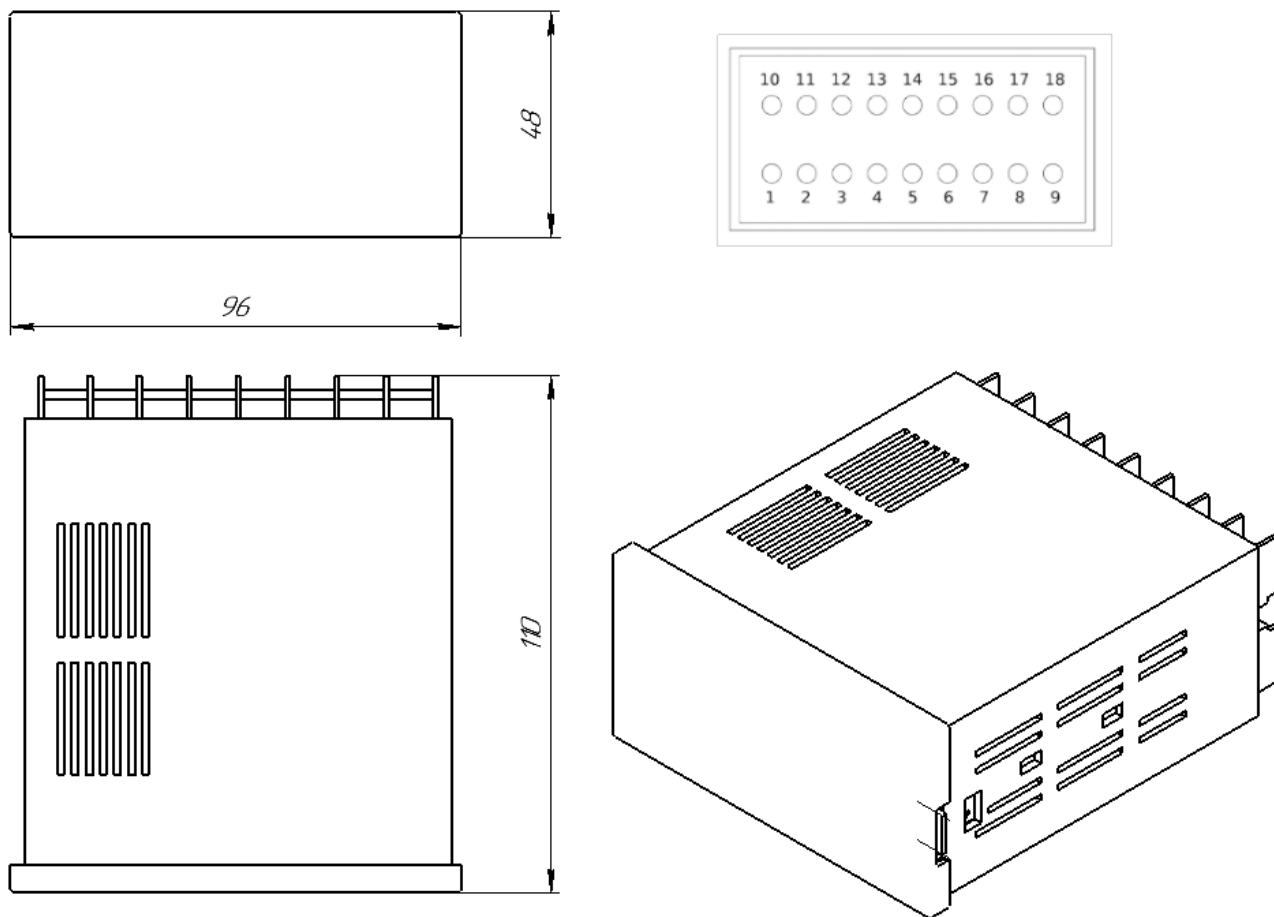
Габаритные и установочные размеры, нумерация клемм.
